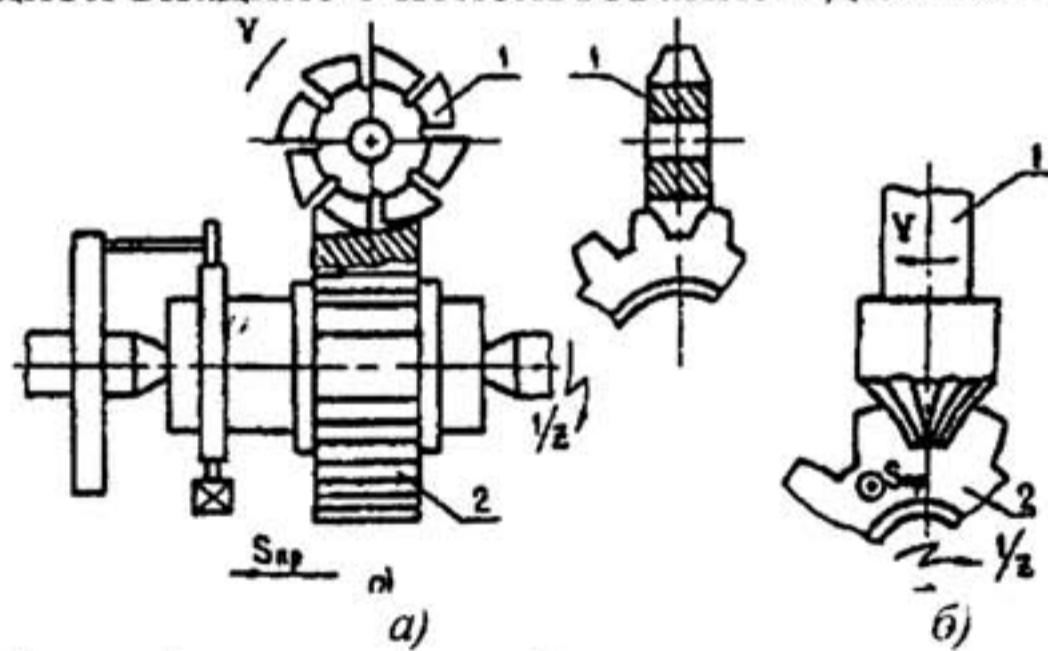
Схемы фрезерования зубчатых колес методом копирования на универсально - фрезерных станках . (1 - фреза, 2 - нарезаемое колесо)
